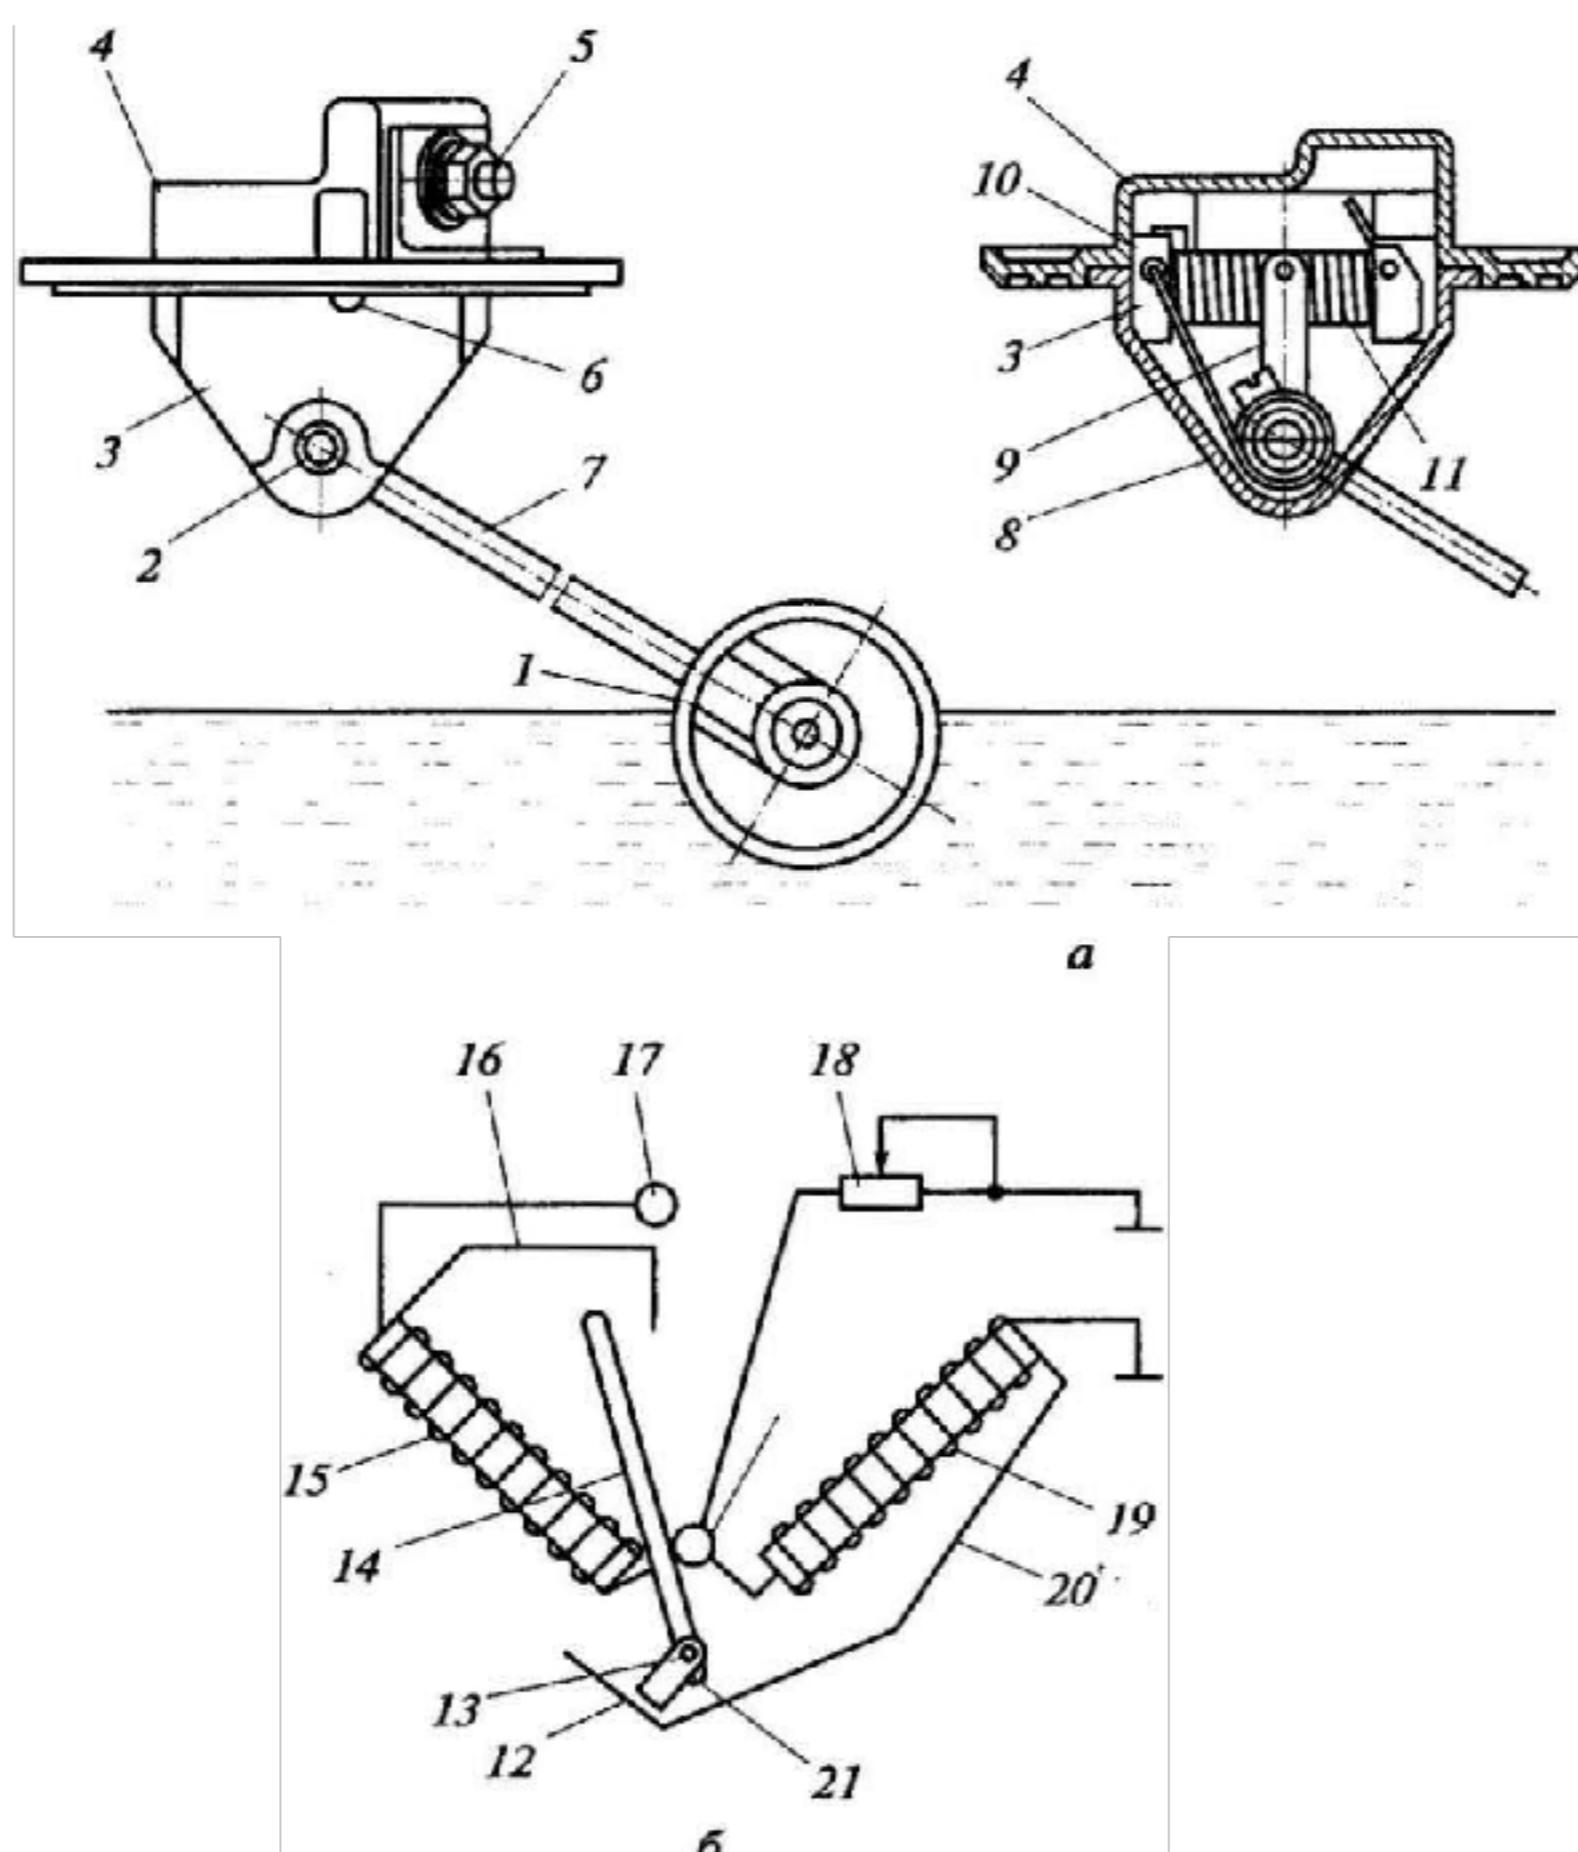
Электромагнитный указатель уровня топлива: а — датчик; б — схема указателя; 1 — поплавок; 2 — ось ползунка реостата; 3 — нижняя часть корпуса; 4 — верхняя часть корпуса; 5 — выводной контакт; 6 — винт крепления; 7 — рычаг поплавка; 8 — проволочная петля; 9 — подвижный контакт (ползунок) реостата; 10 — пластина реостата; 11 — обмотка реостата; 12, 16, 20 — полюсный наконечник указателя; 13 — противовес стрелки указателя; 14 — стрелка указателя; 15, 19 — обмотки указателя; 17 — входной контакт питающего напряжения; 18 — реостат; 21 — якорек; 22 — контактный зажим
